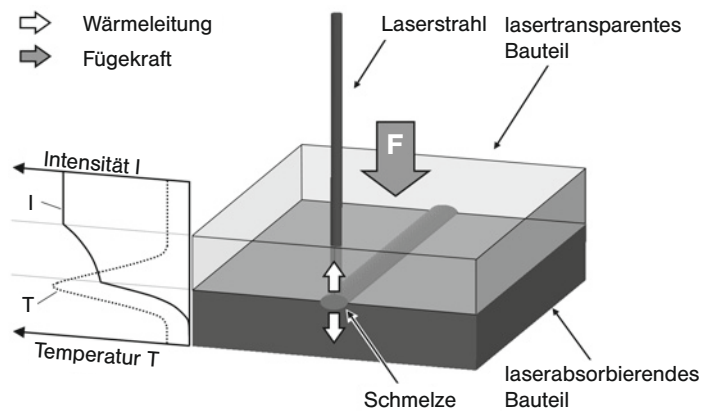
Prinzip des Laserdurchstrahlschweißens
